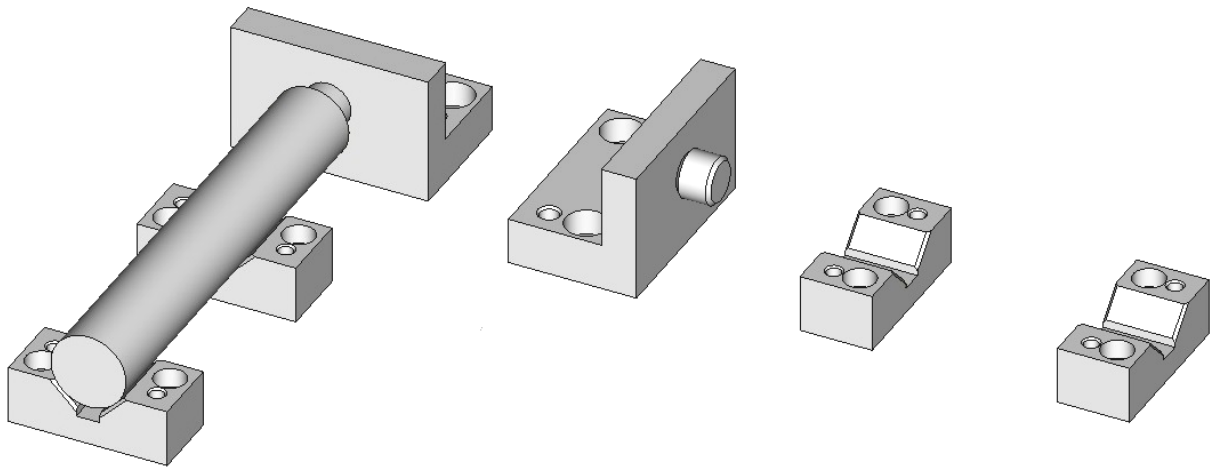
Цилиндрическая заготовка на призмах:
